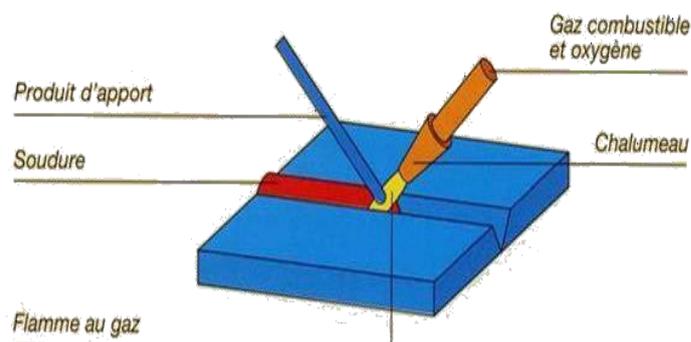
Principe du soudage oxygaz [3].
